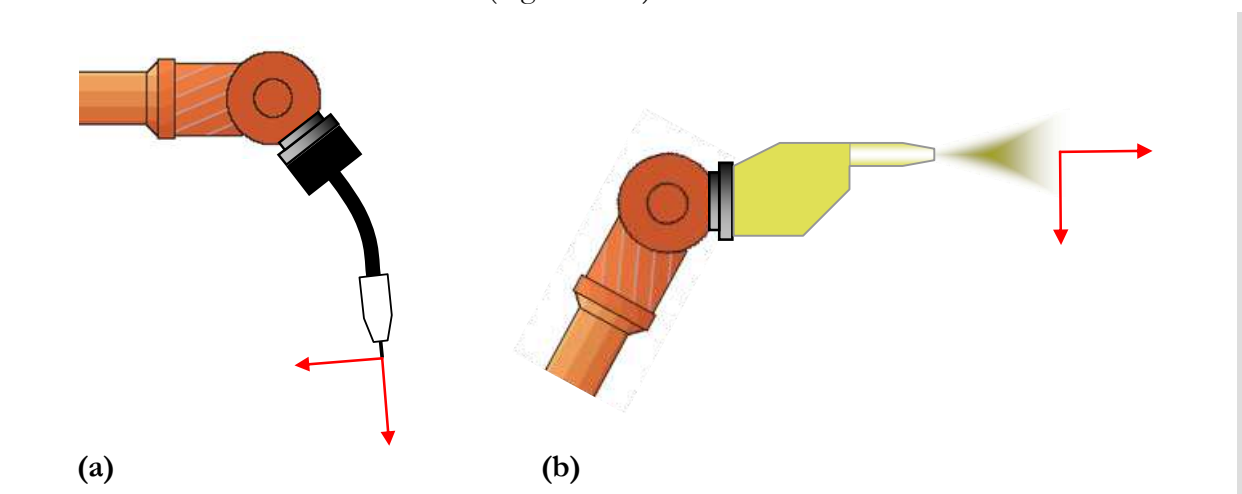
Emplacements de repère outil : en soudage (a) et en peinture (b)
